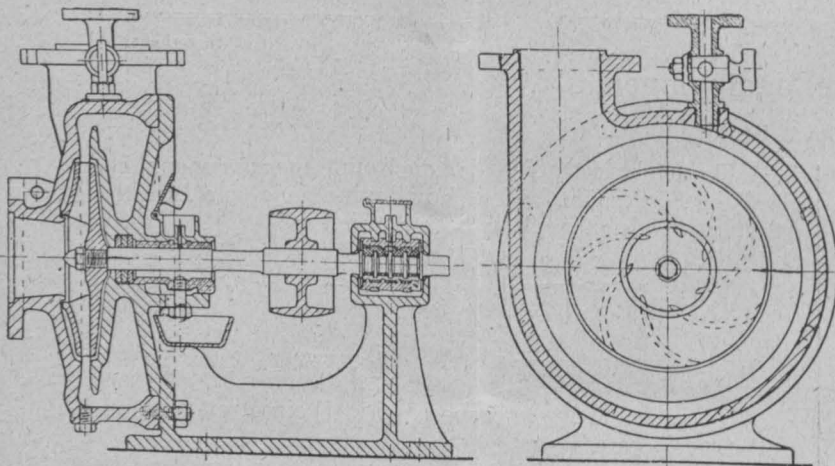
Längenschnitt und Querschnitt der Decoeurschen Pumpe
